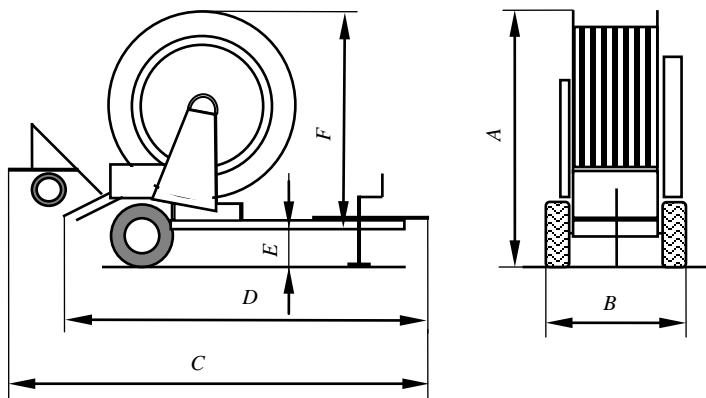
Габаритный чертеж шлангового дождевателя
